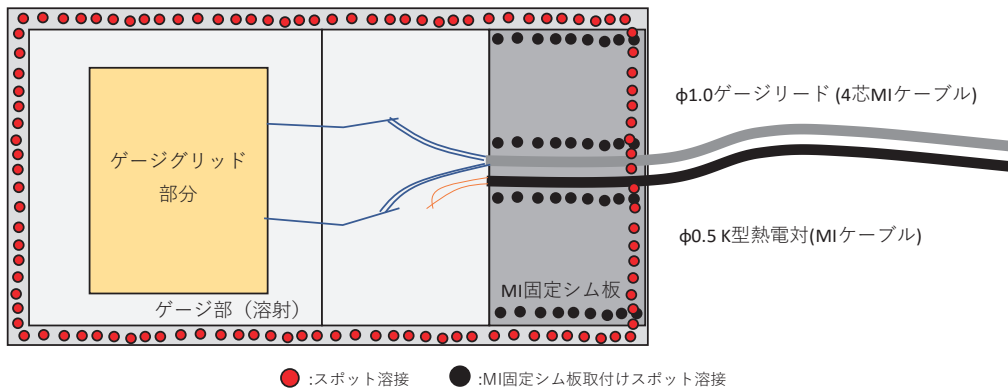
溶接型溶射ひずみゲージの施工平面図
